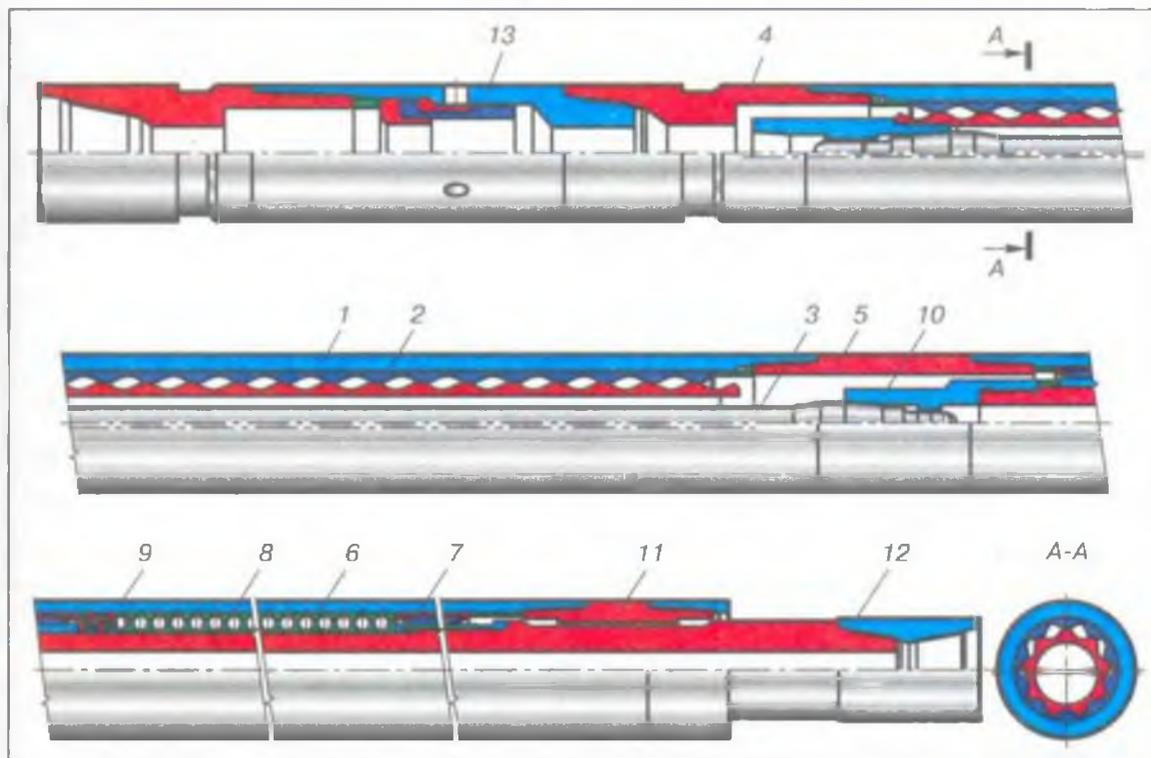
Многозаходный винтовой забойный двигатель: 1 – статор; 2 – ротор; 3 – гибкий вал (торсион); 4, 5 – верхний и соединительный переводники; 6 – многорядная упорная шаровая опора; 7 – радиальный подшипник; 8 – вал шпинделя; 9 – корпус шпинделя; 10 – полумуфта вала; 11 – шпиндель; 12 – наддолотный переводник; 13 – переливной клапан.
